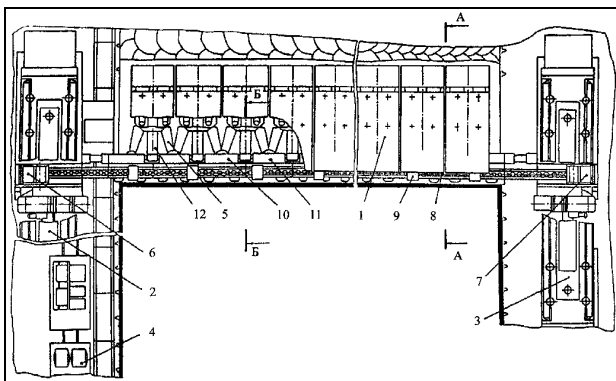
Агрегат очисний фронтальний АФК: 1, 2, 3 — механізоване кріплення (1 — лавне; 2, 3 — сполучення); 4 — енергопоїзд; 5 — портал; 6, 7 — структурні елементи; 8 — ланцюг; 9 — стругові каретки; 10, 11 — секції базової балки; 12 — штовхач базової балки.
